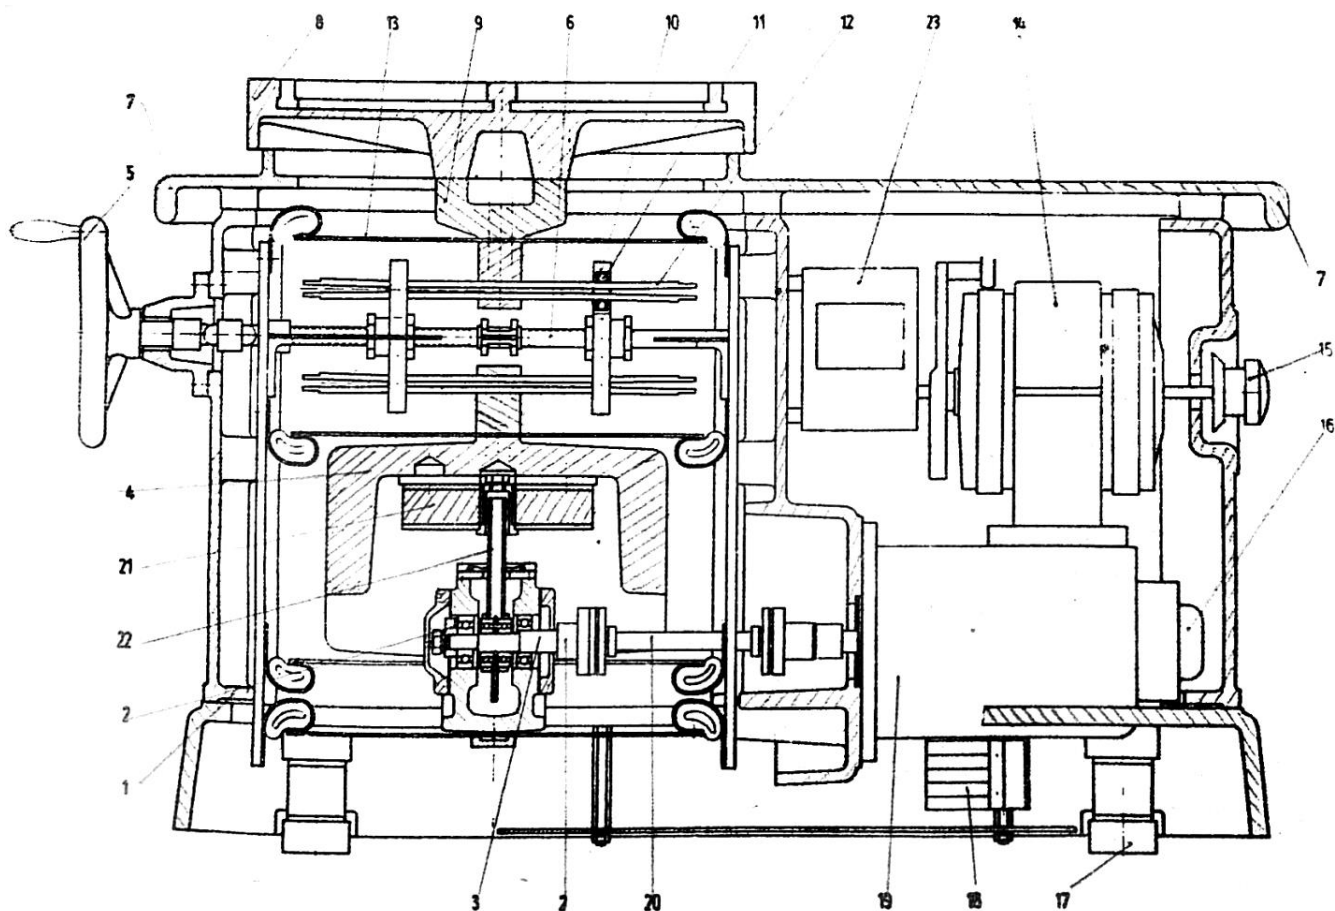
Креслення вібростолу: 1 - корпус; 2 - контрваги; 3 - ексцентриковий вал; 4 - контрмаса; 5 - маховик; 6 - перестановочний шпindel; 7 - верхня перекриваюча плита; 8 - стіл для прикріплення об'єкта; 9 - рама столу; 10 - пружинні повзунки; 11 - ковзаючі ролики; 12 - дві пари пружин; 13 - підтримуюча пружина; 14 - регулювальний трансформатор; 15 - поворотна кнопка; 16 - датчик числа обертів; 17 - ножні рейки з гумовим буфером; 18 - реле; 19 - приводний двигун; 20 - зчеплення; 21 - збудлива пружина; 22 - ексцентриковий штовхач; 23 - тримач вимірювального приладу; 30 - щит з написом «увага»; 31 - шкала довжини пружин; 32 - вимірювальний клин; 33 - частотомір; 34 - контрольна лампа; 35 - натискна клавіатура "включ."; 36 - натискна клавіатура "вимикач."; 37 - тримач мікроскопа, угвинчується; 38 - затискна гільза; 39 - затискний гвинт; 40 - мікроскоп; 41 - зубчастий привід
